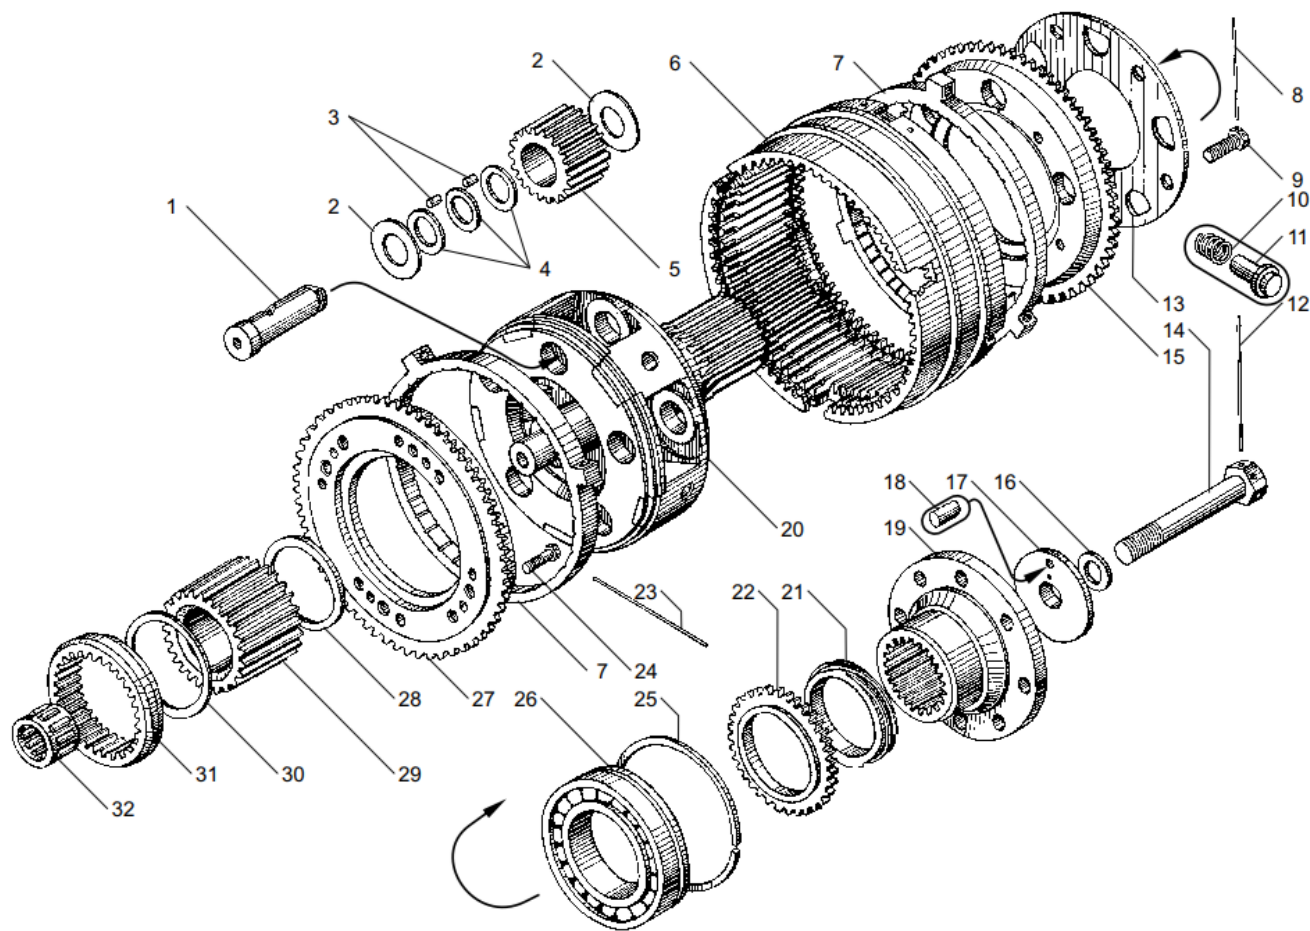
ВАЛ И ШЕСТЕРНИ ДЕМУЛЬТИПЛИКАТОРА КОРОБКИ ПЕРЕДАЧ
